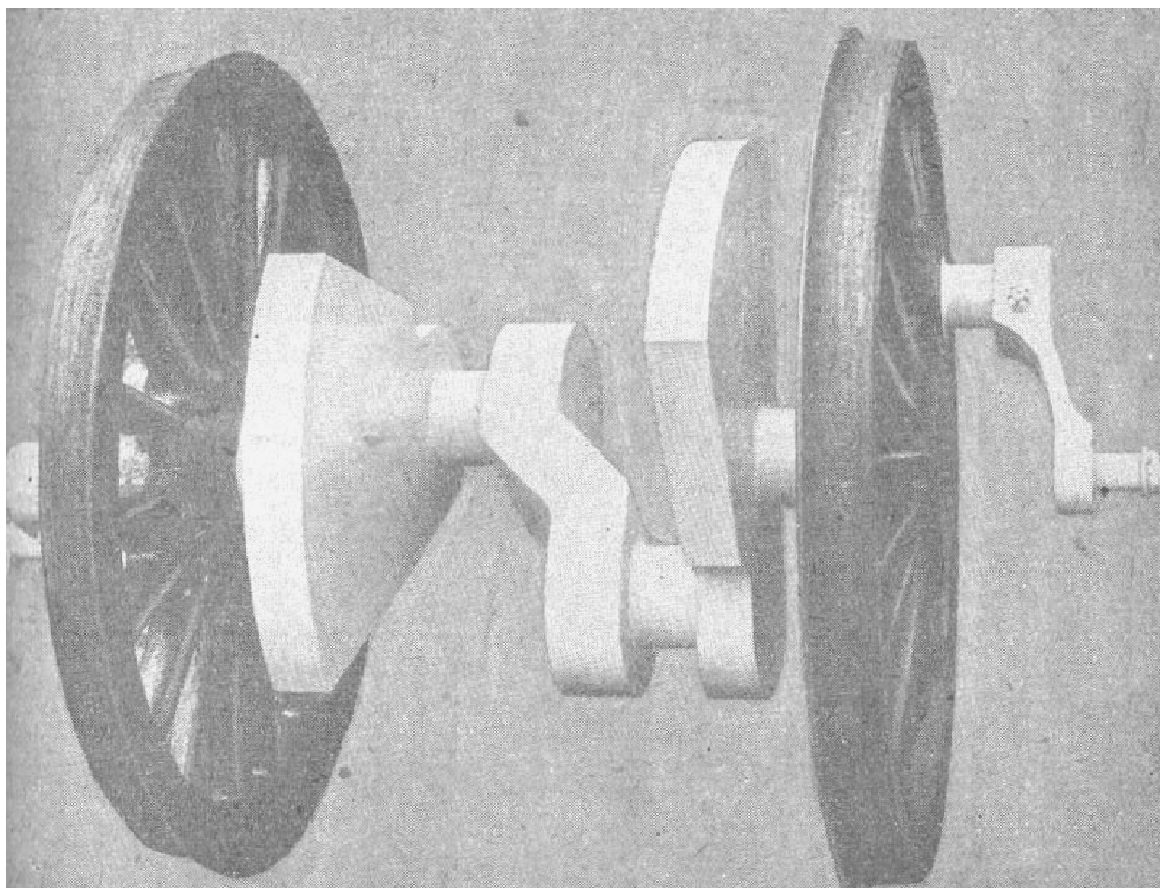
Eje acodado polyblock parcialmente auto-equilibrado, en 7 piezas, del P.L.M.
